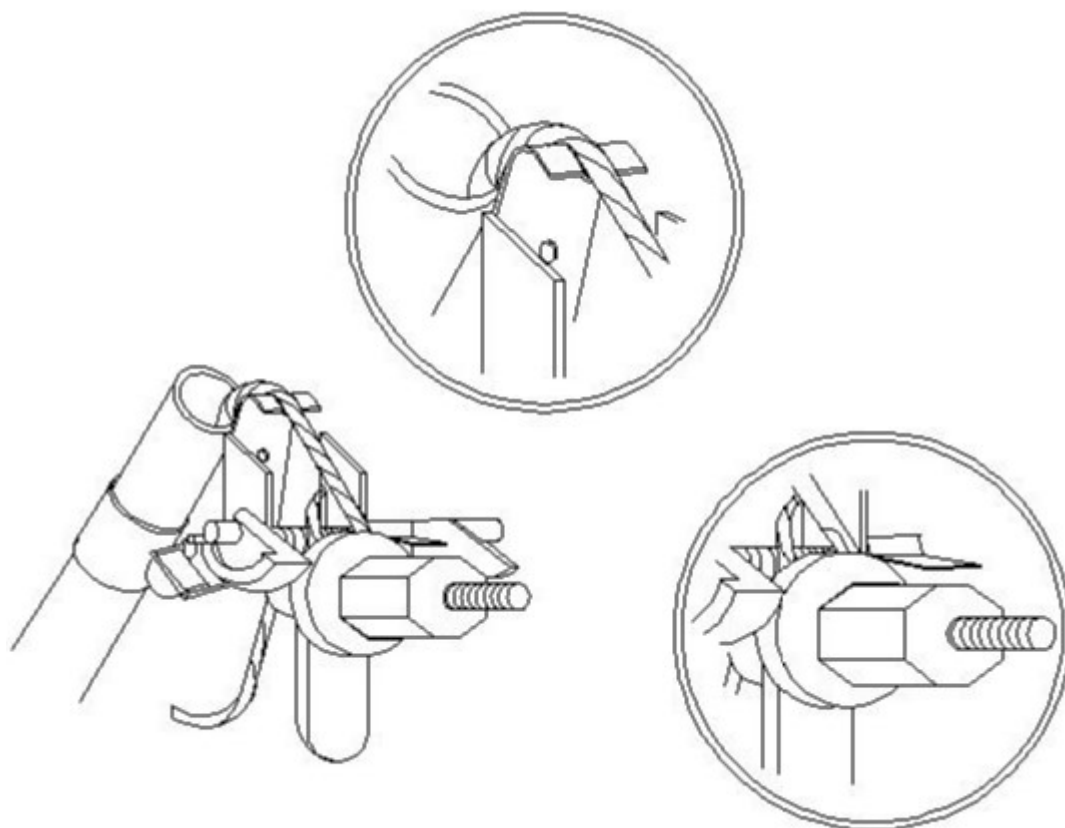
Detalle fijación elemento fusible a la base del tubo porta f
